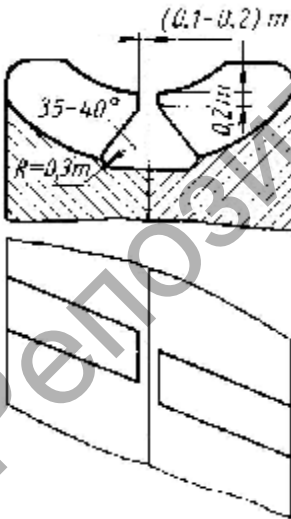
Форма обода червячного колеса при малом числе зубьев [37]
